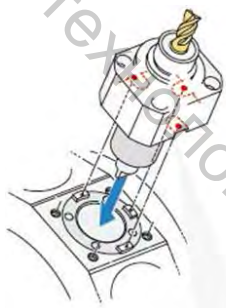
Резцовый блок для установки резцов на станке с ЧПУ:
